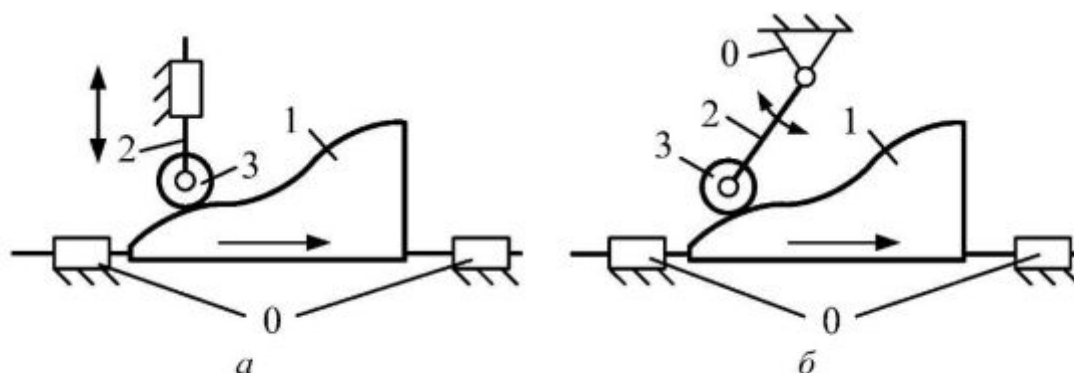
Схемы кулачковых механизмов с поступательным движением кулачка
